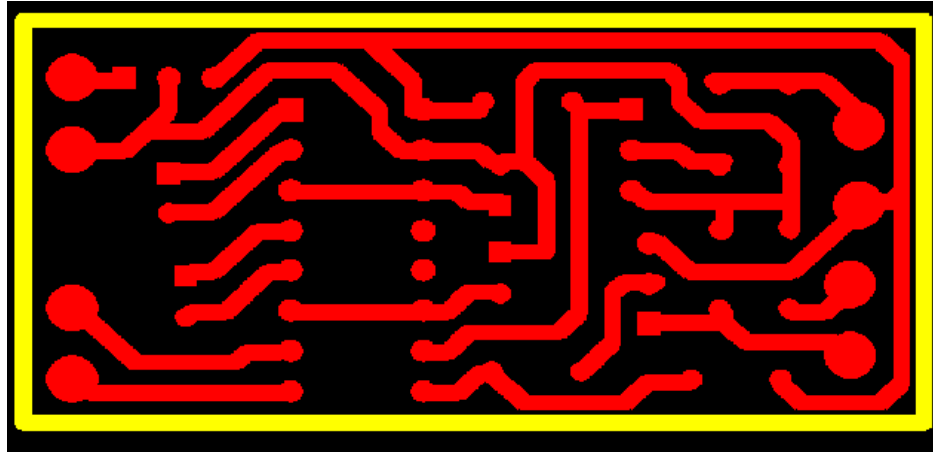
Tarjeta electrónica de la interfaz, cara de soldadura.
